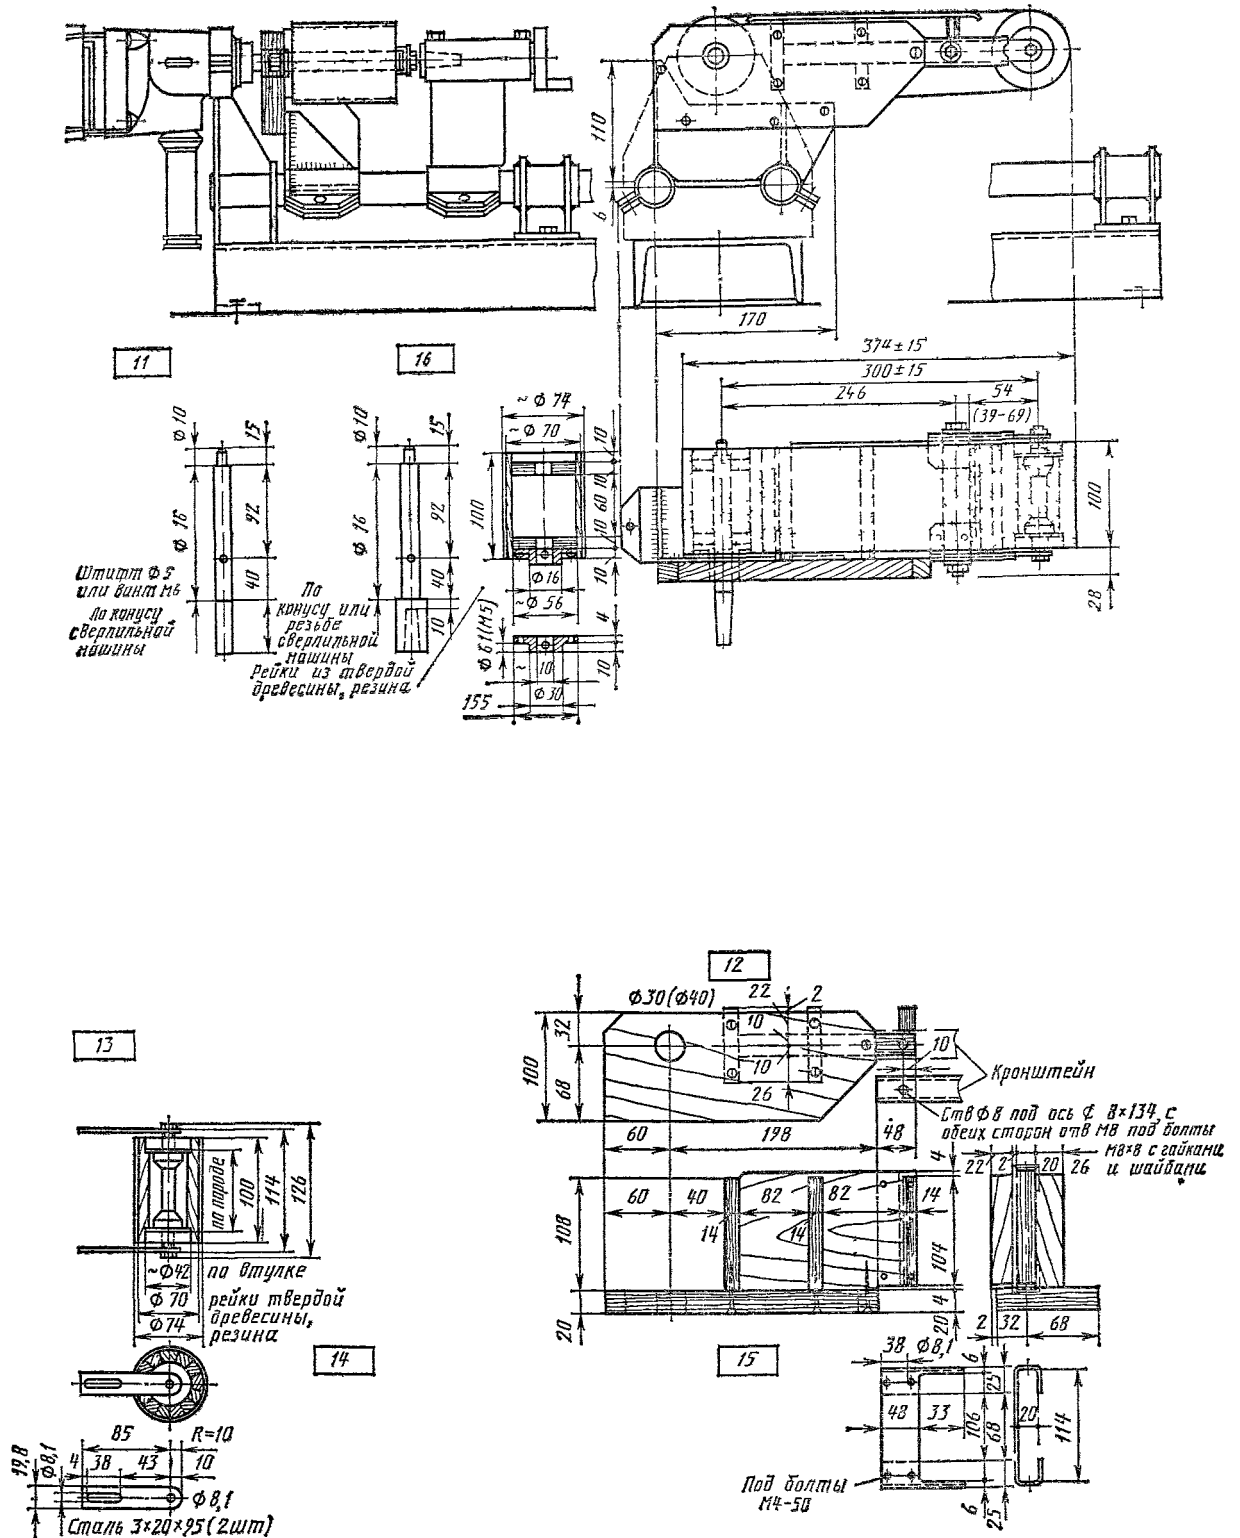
Ленточно-шлифовальный станок (на базе станка рис. 135):
